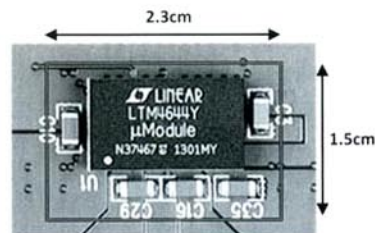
四输出、4A 降压型微型模块稳压器方案占用的 PCB 面积
